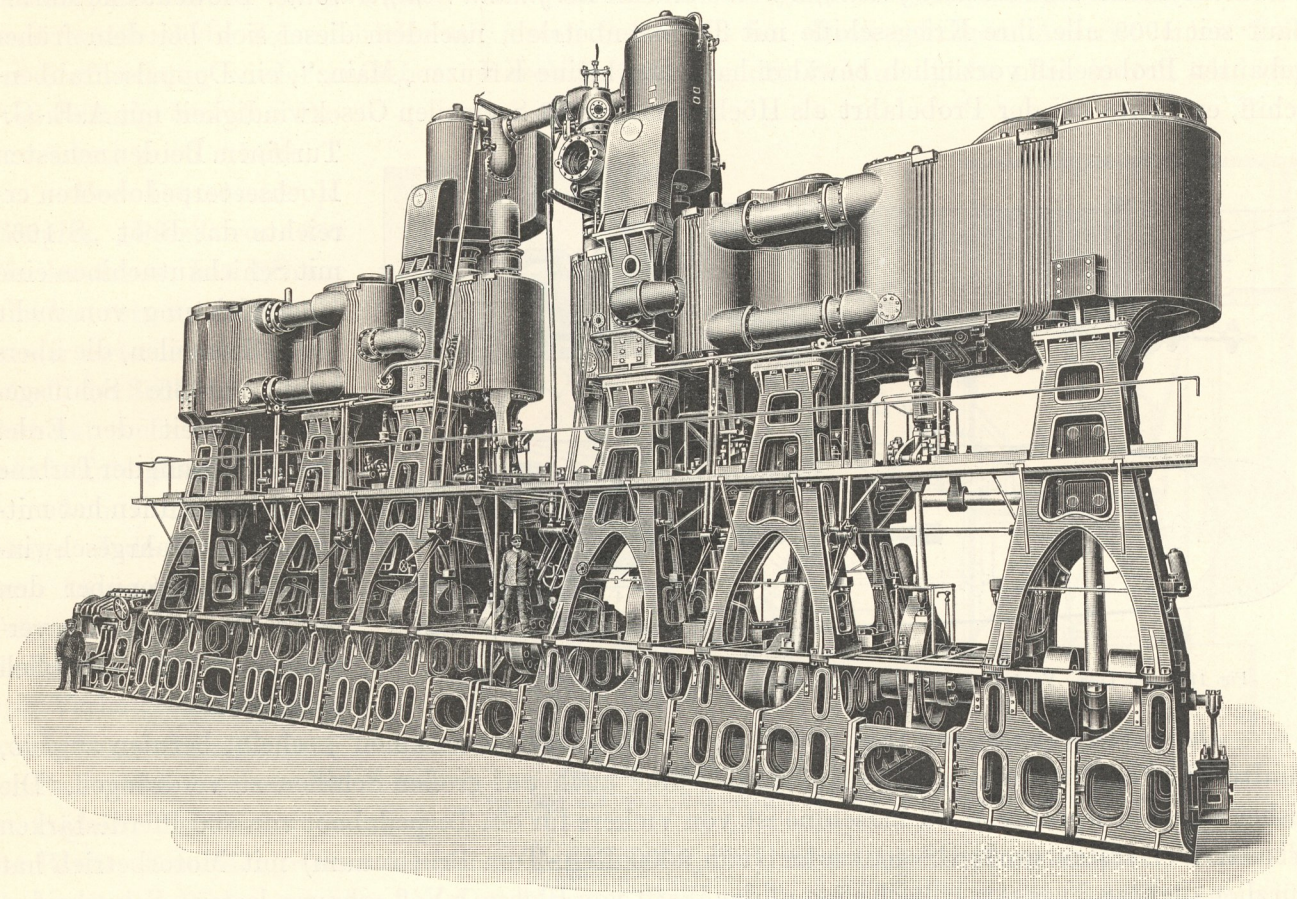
Eine der beiden Vierfach-Expansionsmaschinen des Schnelldampfers „Kaiser Wilhelm II.“, erbaut von der Stettiner Maschinenbau-Aktiengesellschaft „Vulcan“.
